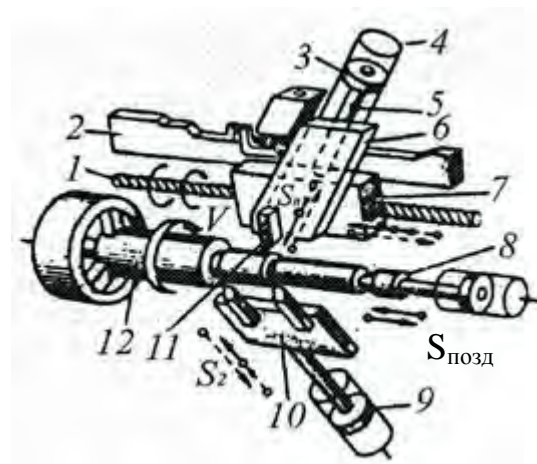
Схема роботи гідрокопіювального напівавтомата
